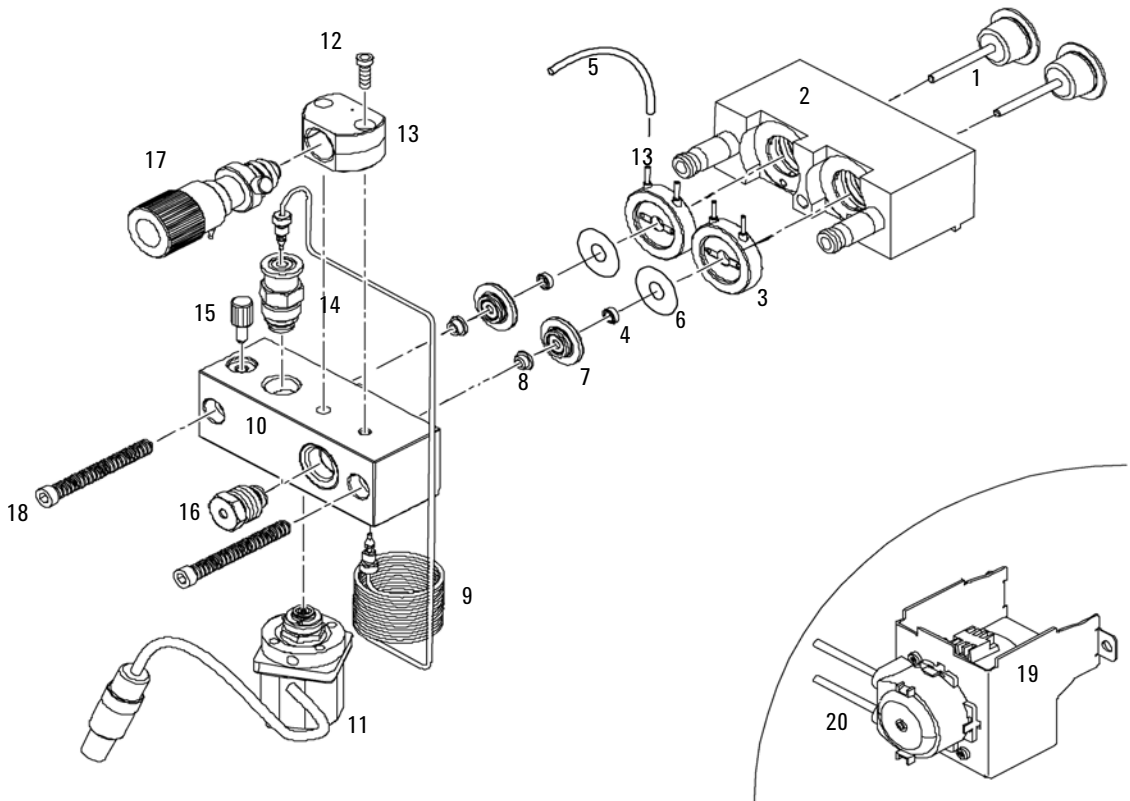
Ensemble tête de pompe avec accessoire de rinçage de joints
